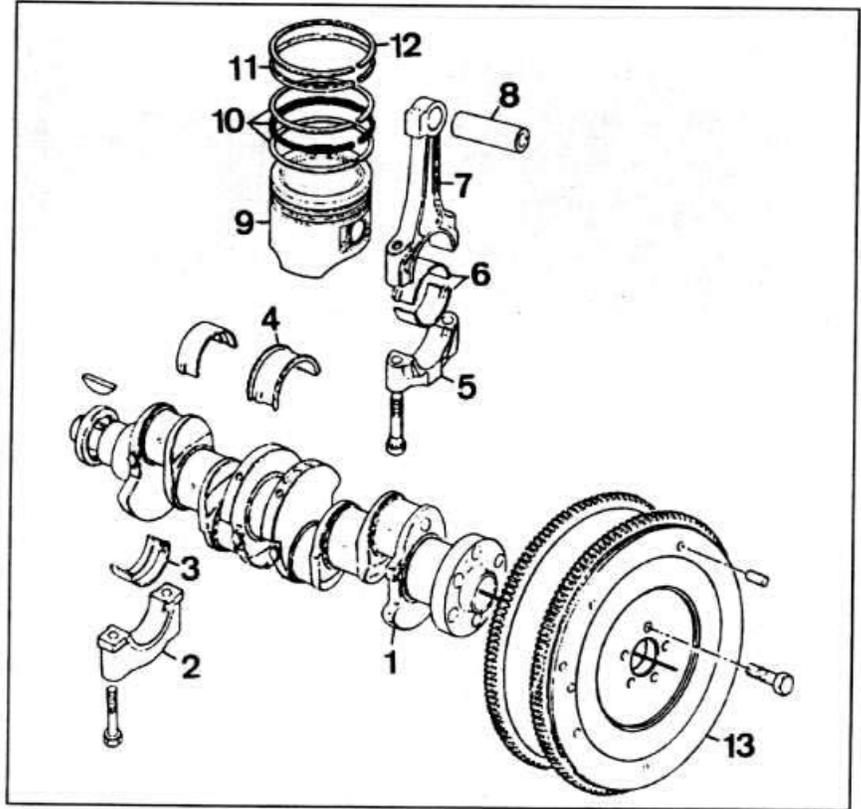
D.61. Кривошипно-шатунный механизм двигателя Zetec.
